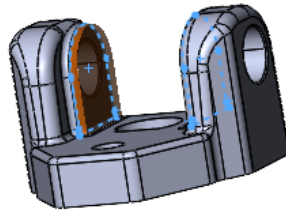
Витягування ескізу на величину припуску (2,5 мм) для створення заготовки.
